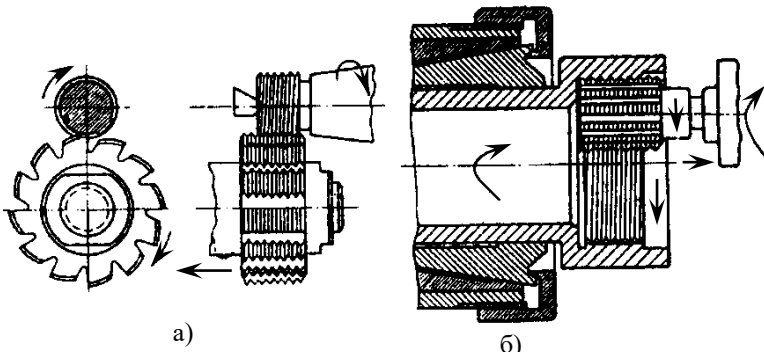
Схема фрезерування різі груповими фрезами:
